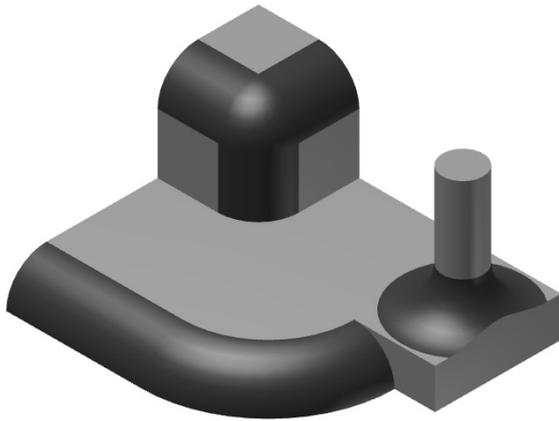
Abrundungen mit Typ KONSTANT (rot markiert)
